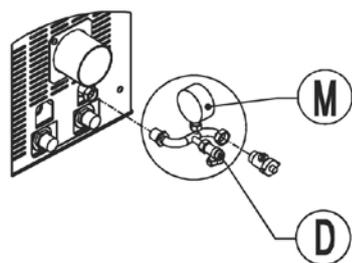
Terminale con rubinetto di caricamento (D) e manometro (M)
